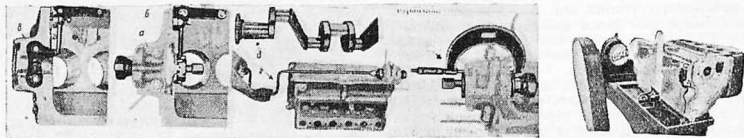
Установка, замеры и обточка галтелей третьего коренного подшипника
